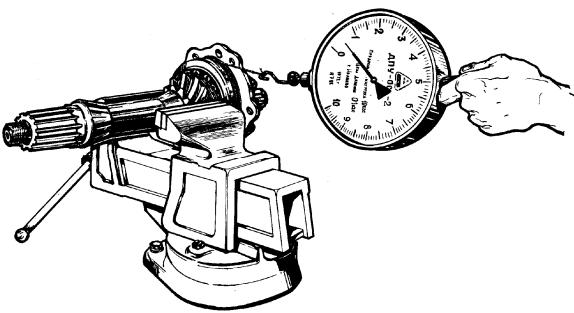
Проверка регулировки подшипников ведущей конической шестерни
